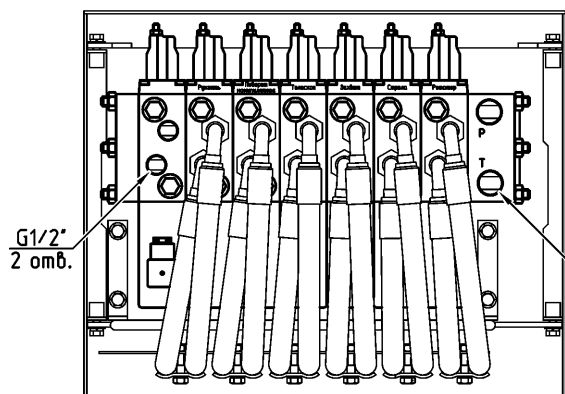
Присоединительные размеры для установки манипулятора
